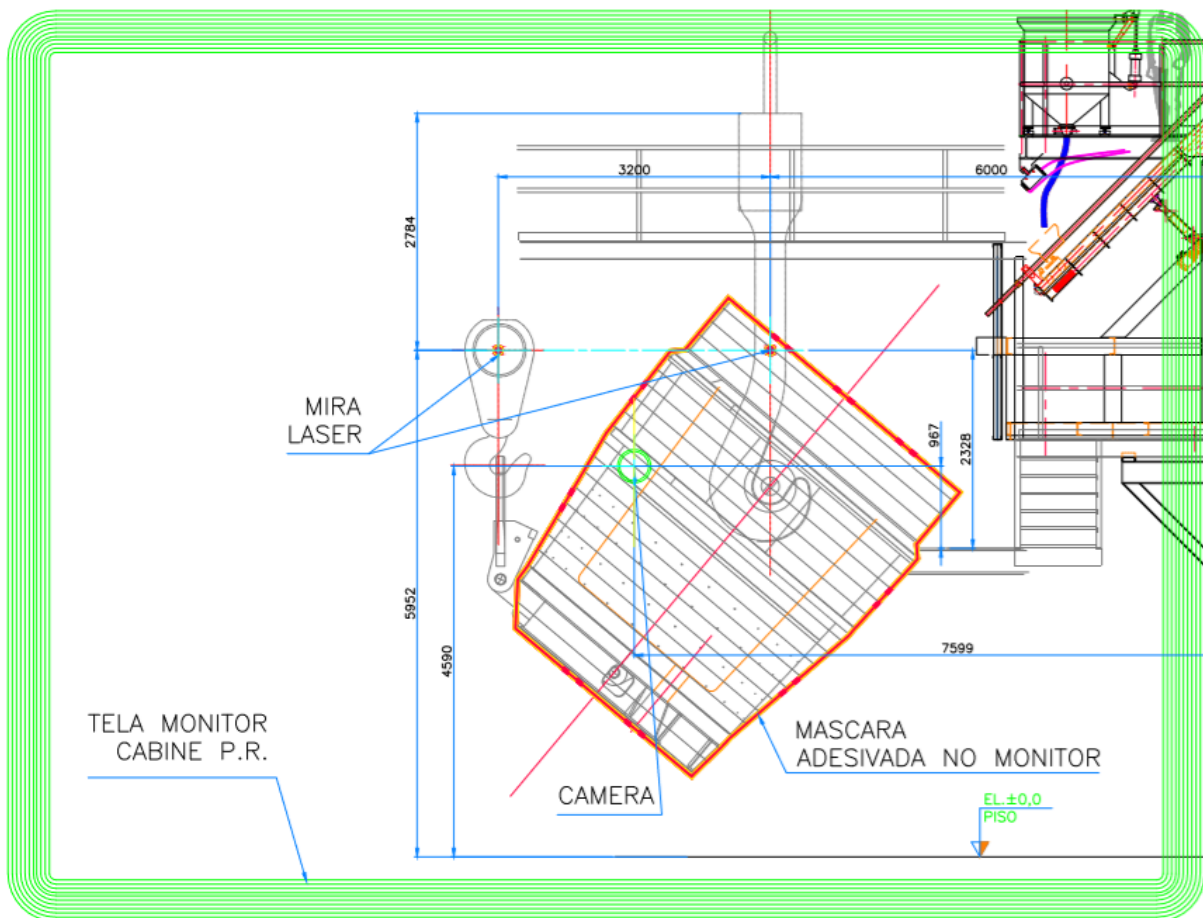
Vista do operador de ponte - Laser e câmera de posicionamento panela
